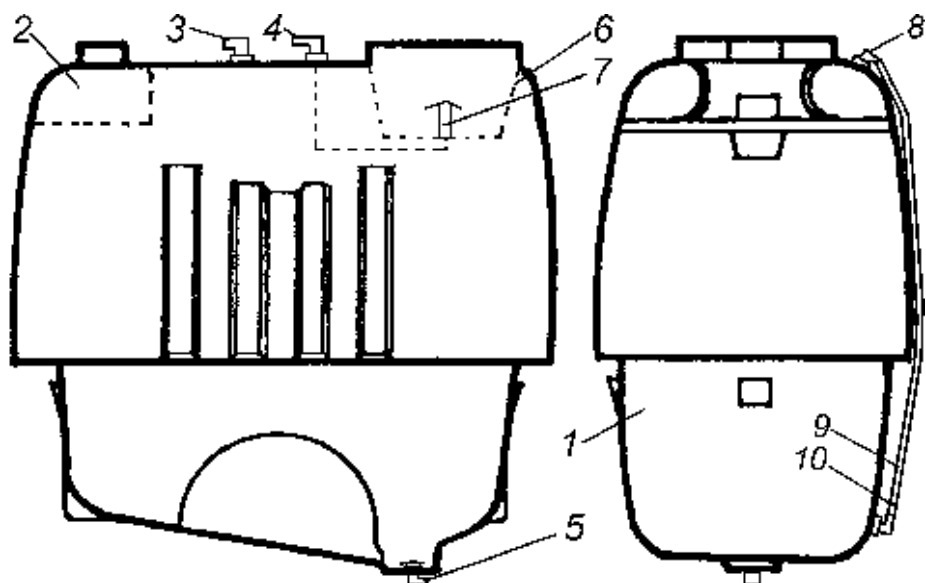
Резервуар опрыскивателя 600, 800 и 1000
